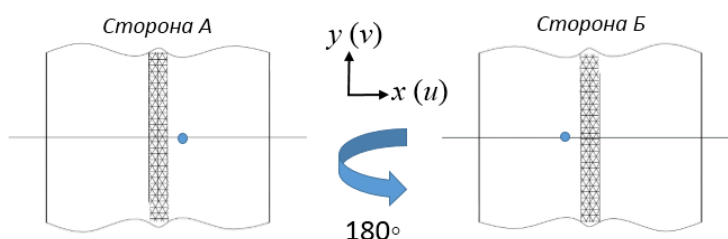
Схема проведения эксперимента и направление измеряемых компонент перемещений относительно линии сварного шва
